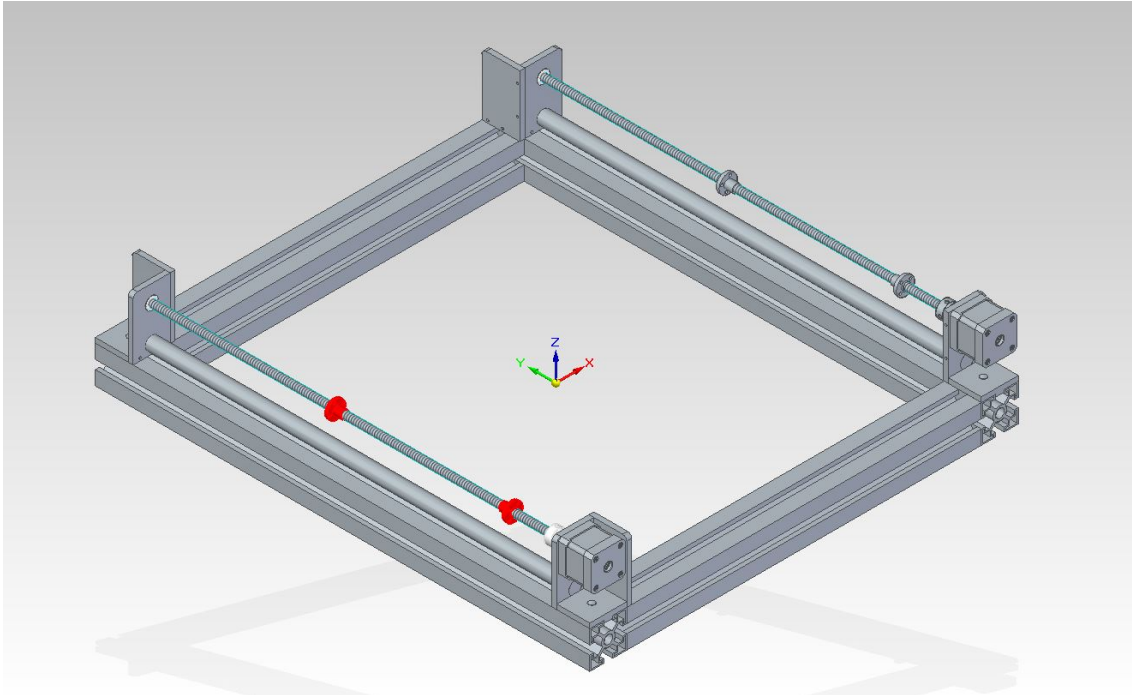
Conjunto con soportes para motores, rodamientos y guía ensamblados.
